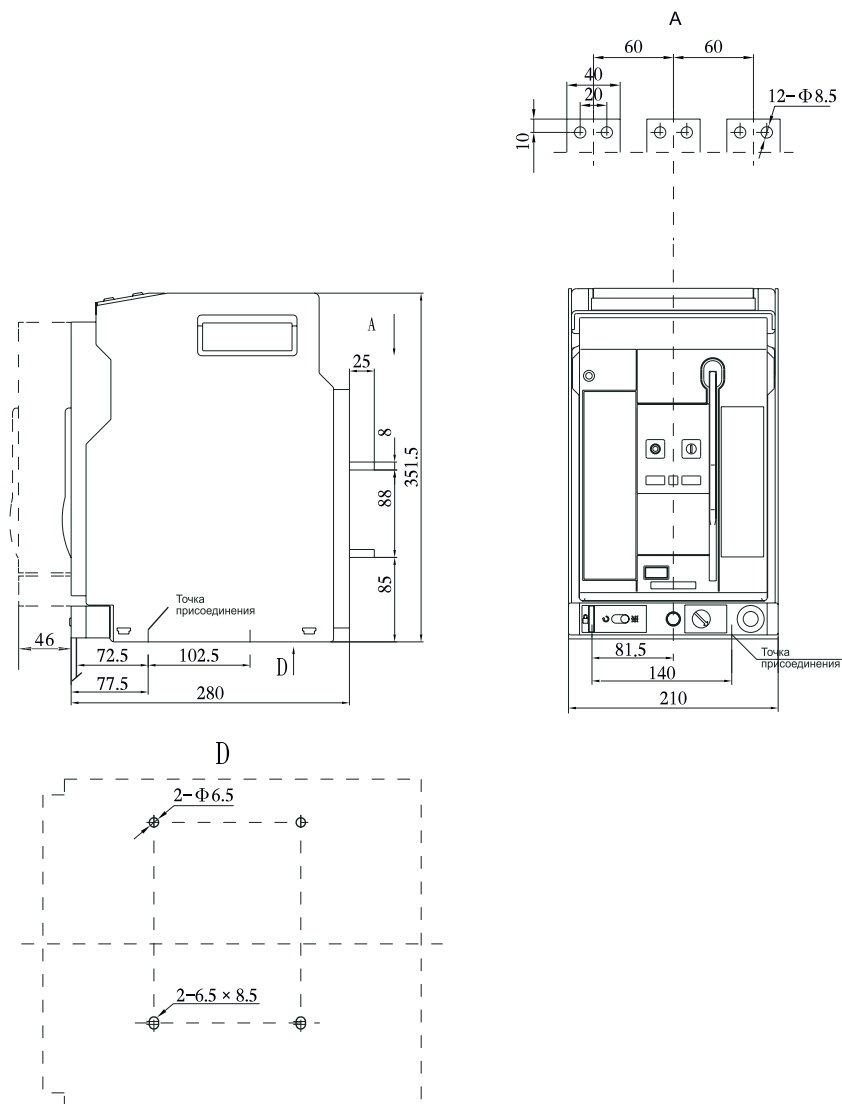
Габаритные размеры выдвижных трехполюсных выключателей типоразмера S
